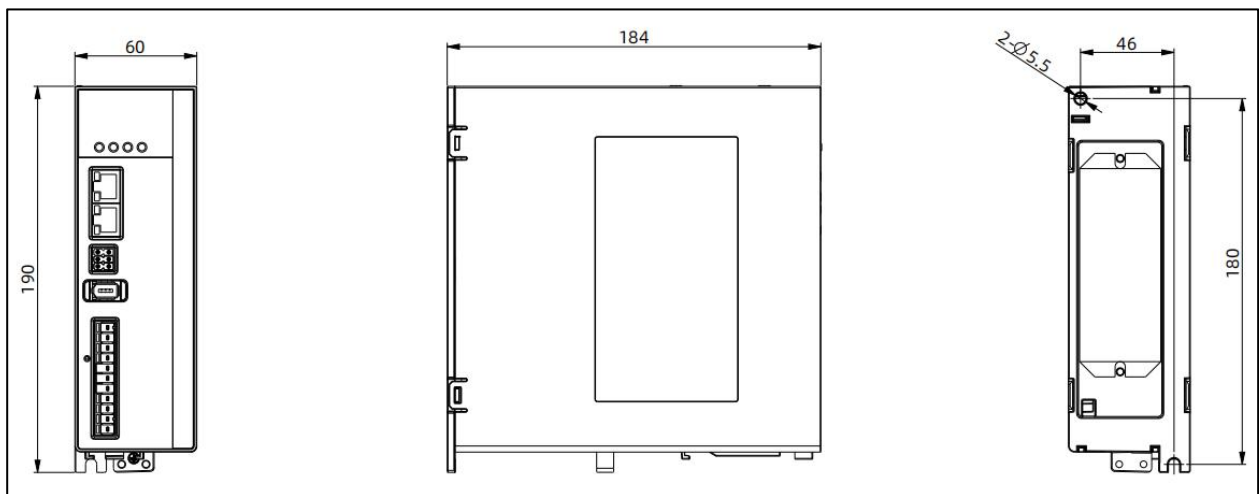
Size B 伺服驱动器安装尺寸 (单位: mm)
